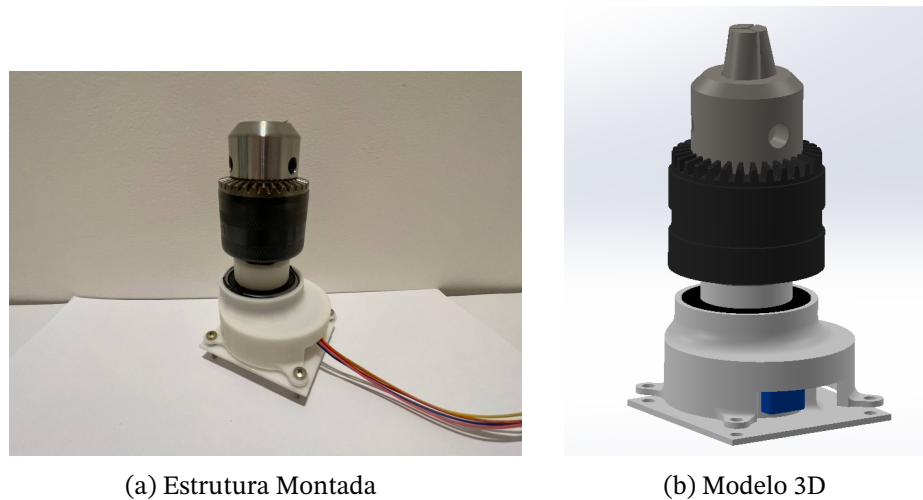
Estrutura Montada para Rotar o Projétil - Fonte: Autor
